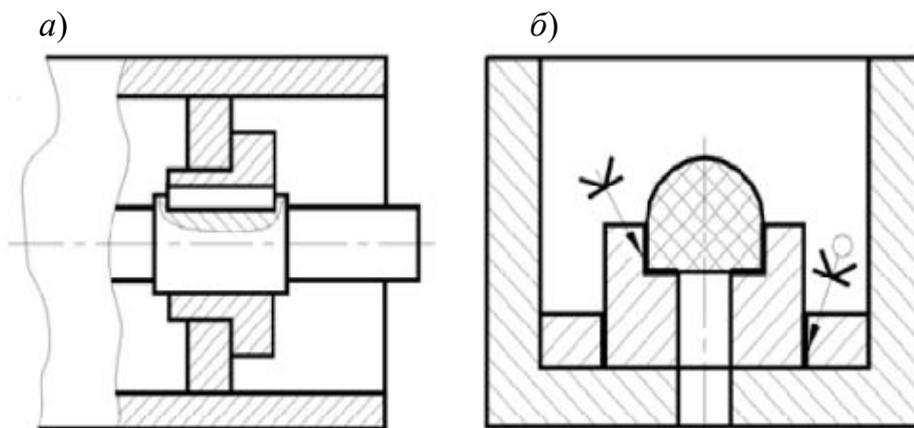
Изображения сварного (а) и клееного (б) соединений в сборе с другими изделиями на чертежах общего вида [23]
